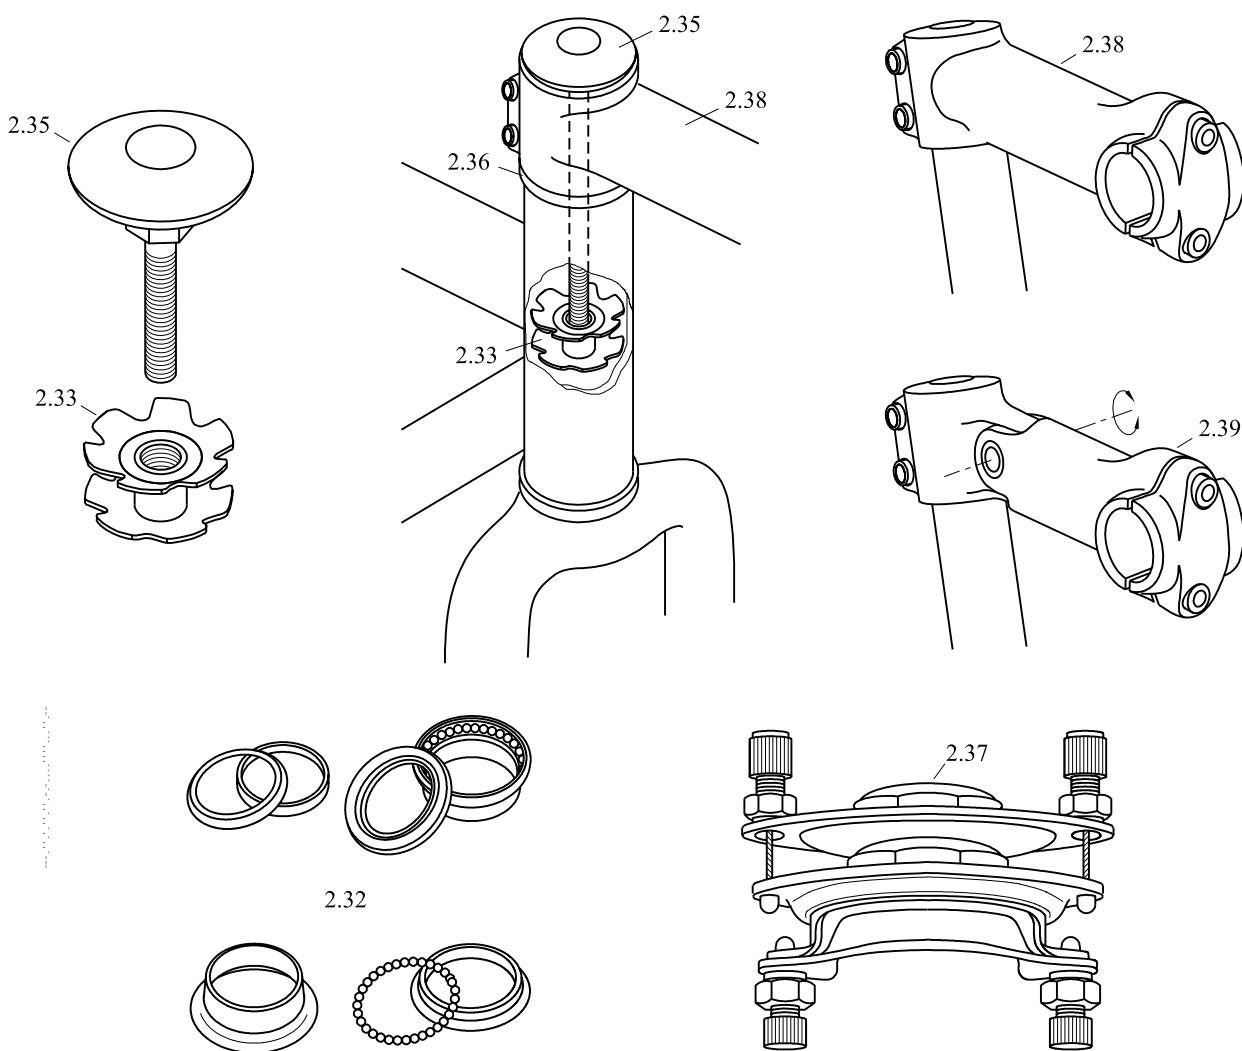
Ensemble de direction / Head assembly / Steuersatz und Lenkung / Gruppo sterzo / Balhoofd samenscholing
